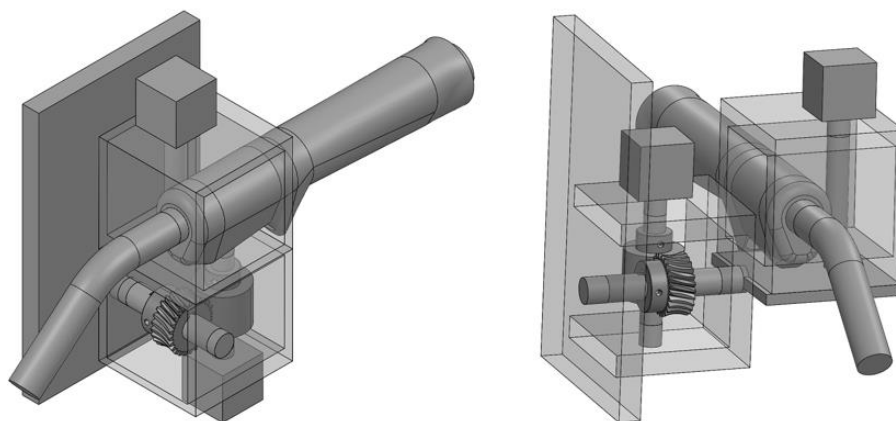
Primeiras montagens do mecanismo de soldadura.
